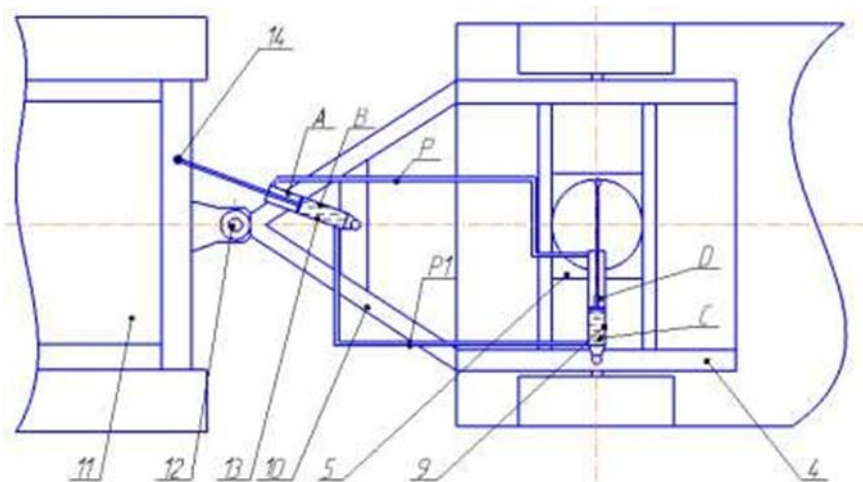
Тягово-зчіпний пристрій причепа з поворотною платформою, що поперечно переміщується – вигляд зверху
